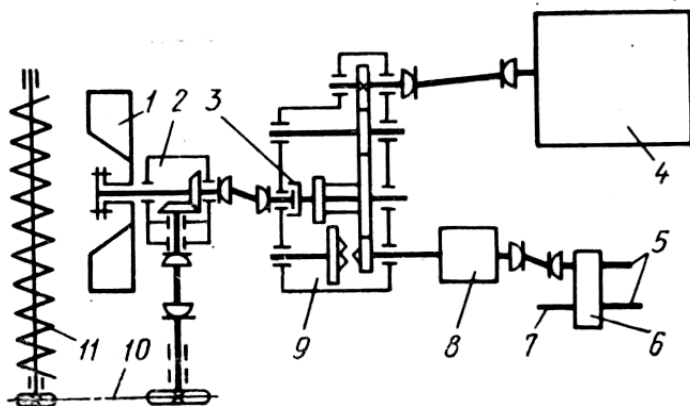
Кинематическая схема одномоторного шнеко-роторного снегоочистителя:
